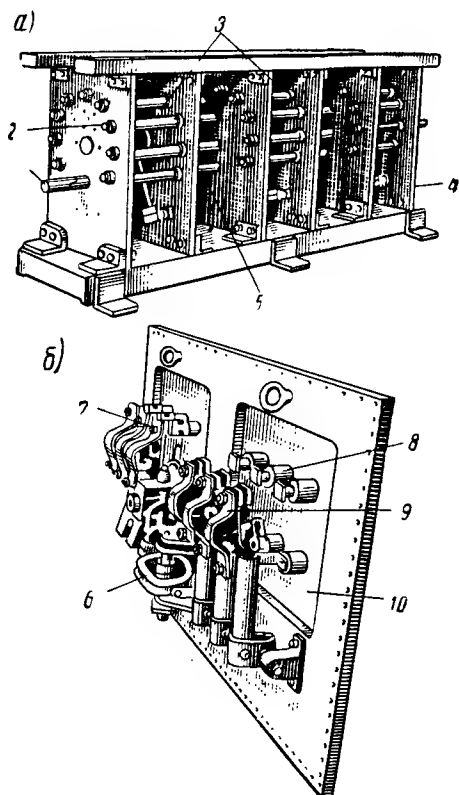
Внешний вид переключателя и контактора переключающего устройства типа РНТ-13
